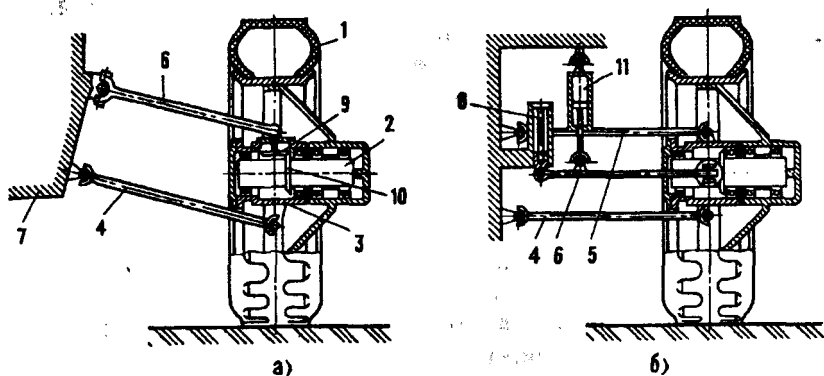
Кинематическая схема колесно-шагающего механизма с интегральной схемой привода:
